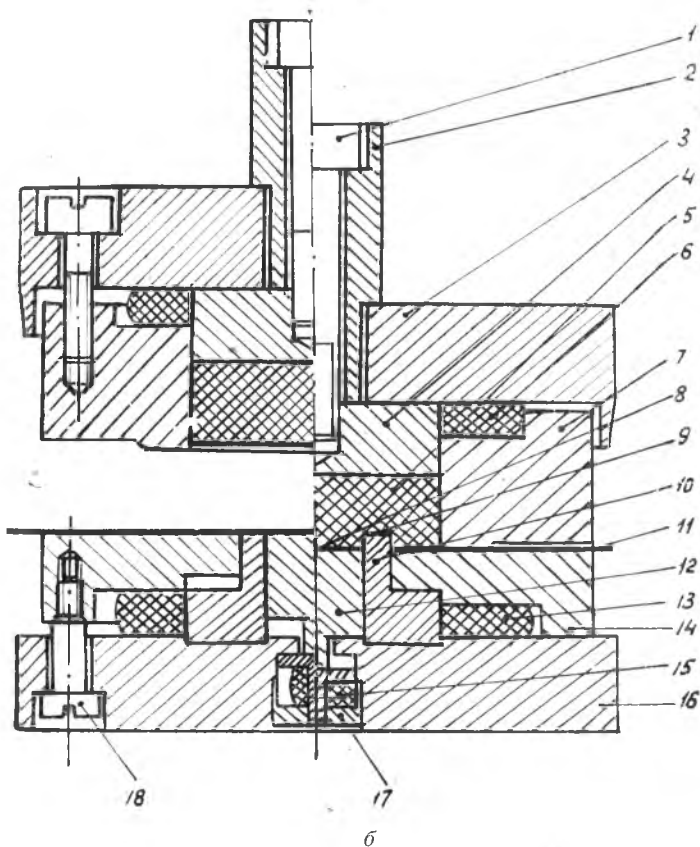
Универсально-переналаживаемый штамп с полиуретаном для вырезки деталей из ленты:
